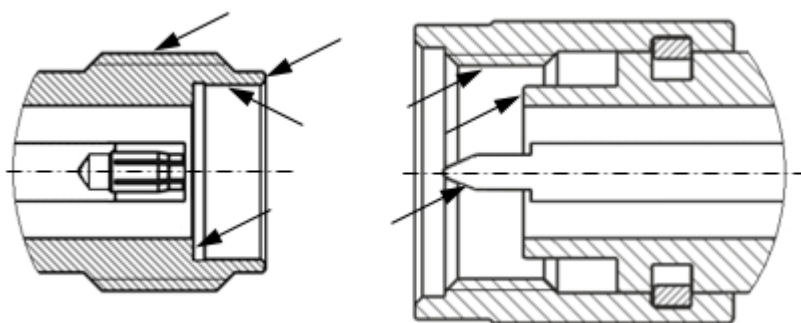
Соединители тип 3,5 мм (розетка и вилка)
